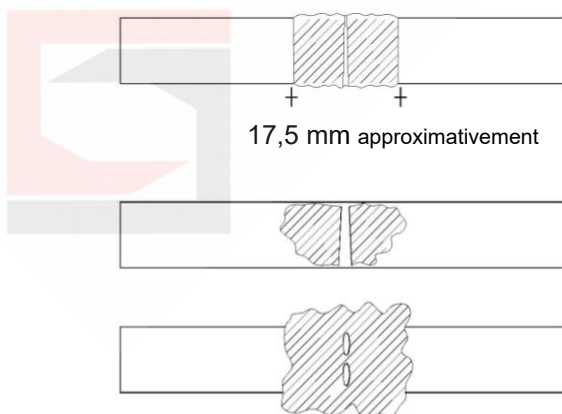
Test préalable pour un temps de soudure adéquat - Illustration
